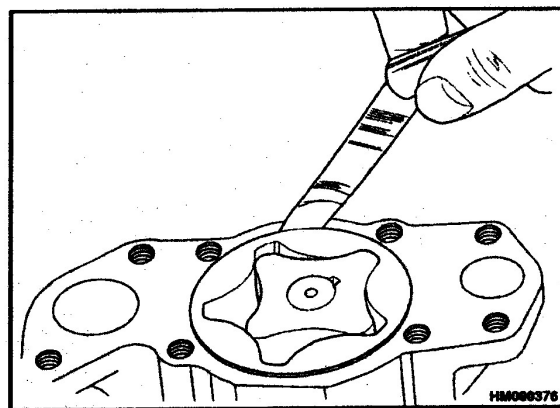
Проверка зазора внешнего рабочего колеса.
